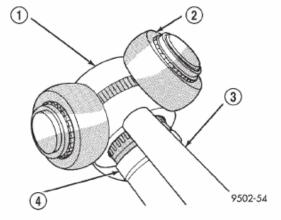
Desmontaje del conjunto de cruceta del eje de interconexión
